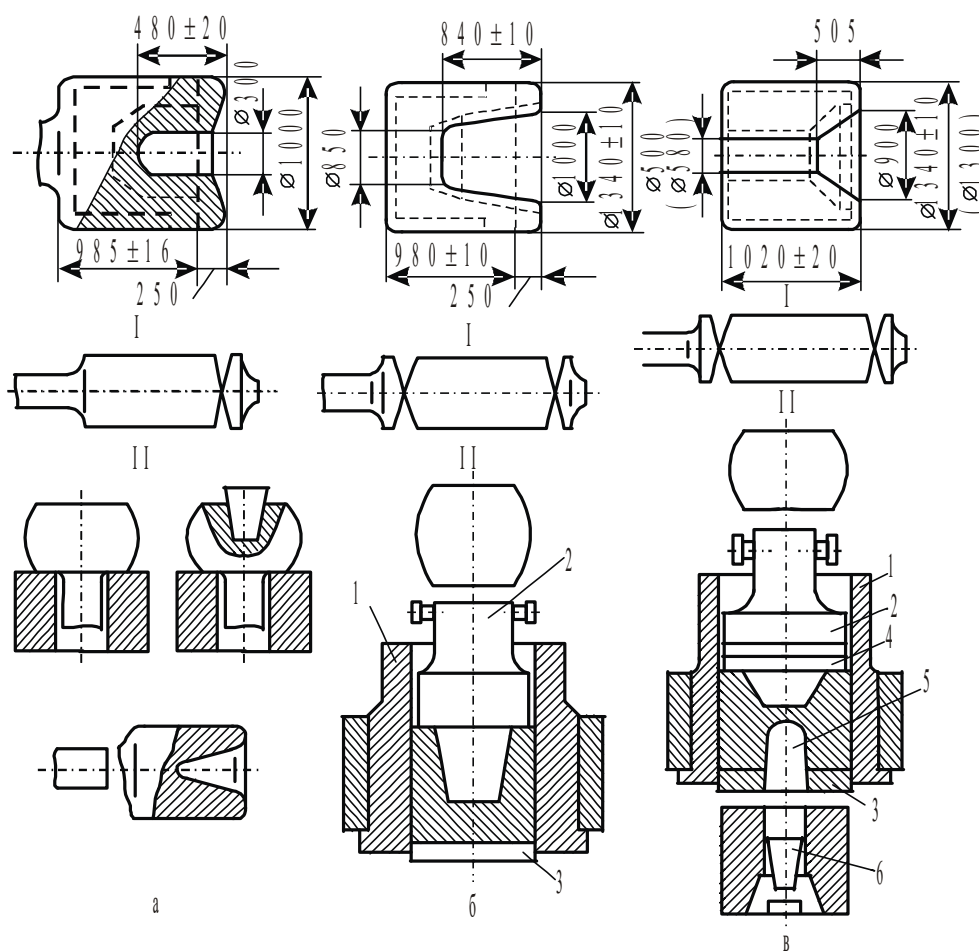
Групова ковка полів поковок: 1 – обойма; 2 – пуансон; 3 – підкладка; 4 – кільця; 5 – прошивень; 6 – спеціальний прошивень; I – попередня обробка злитку; II – осадка та ковка в спеціальному і пересадному інструменті
